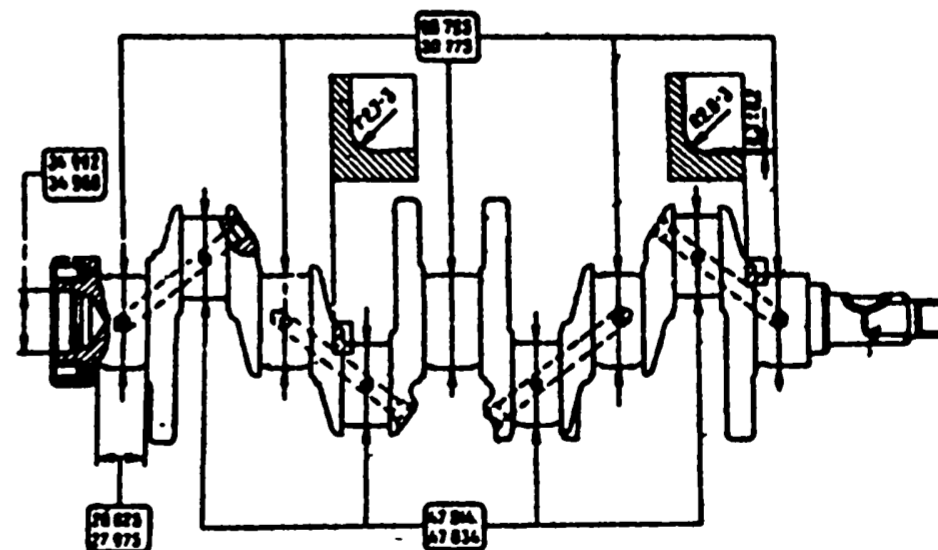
Основные размеры шатунных и коренных шеек коленчатого вала и их галтелей
